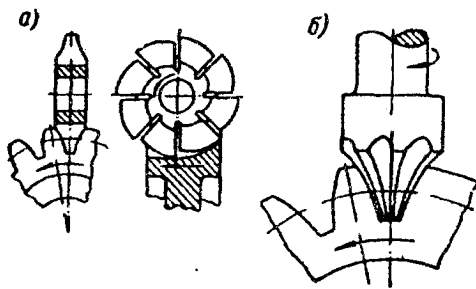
Фрезерування зубців модульними фрезами:
